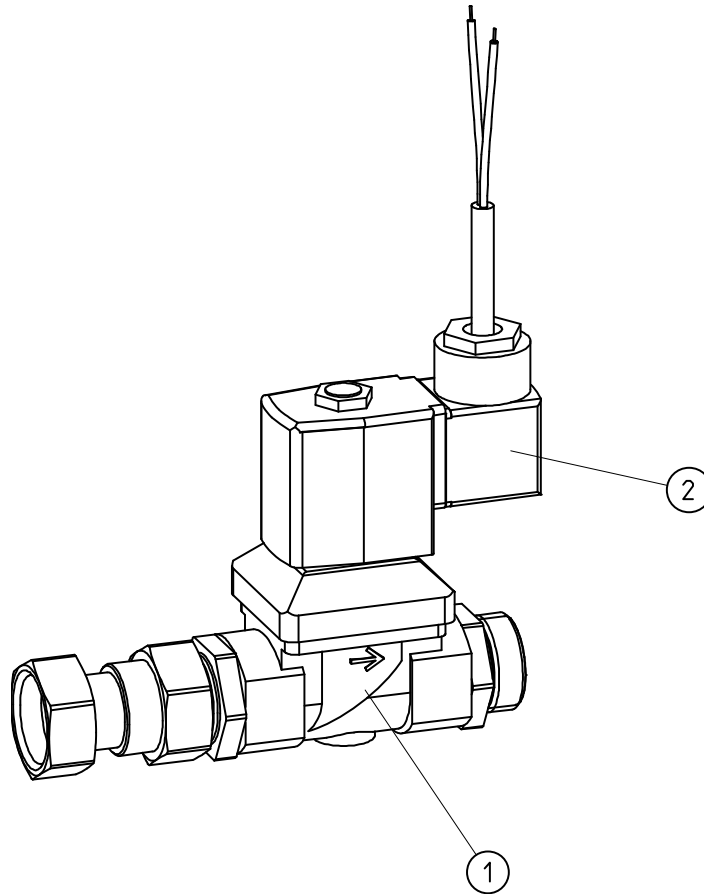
Komponenten GENO-therm Magnetventil kpl. für Koffer Premium
